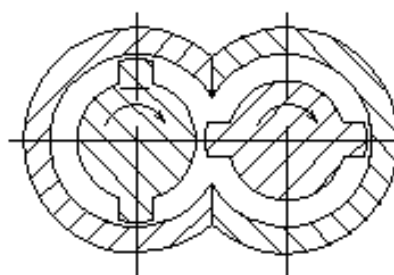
Конструктивные особенности червяков по способу изготовления
